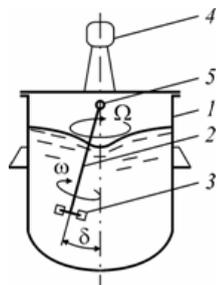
Аппарат с прецессирующей мешалкой: 1 – корпус; 2 – вал; 3 – мешалка; 4 – привод аппарата; 5 – шарнир Гука.
